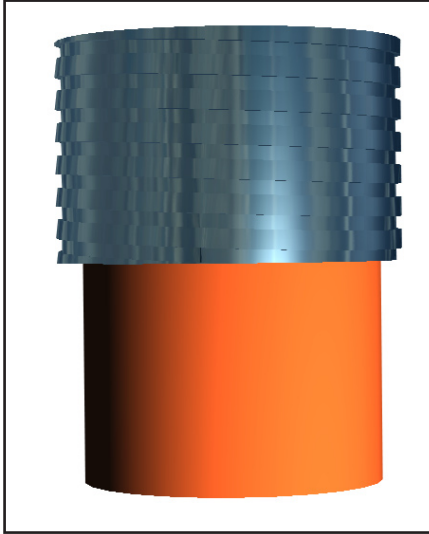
, segmento de tubo (Ø63) roscado, soldado al tubo Ø56 externo.
